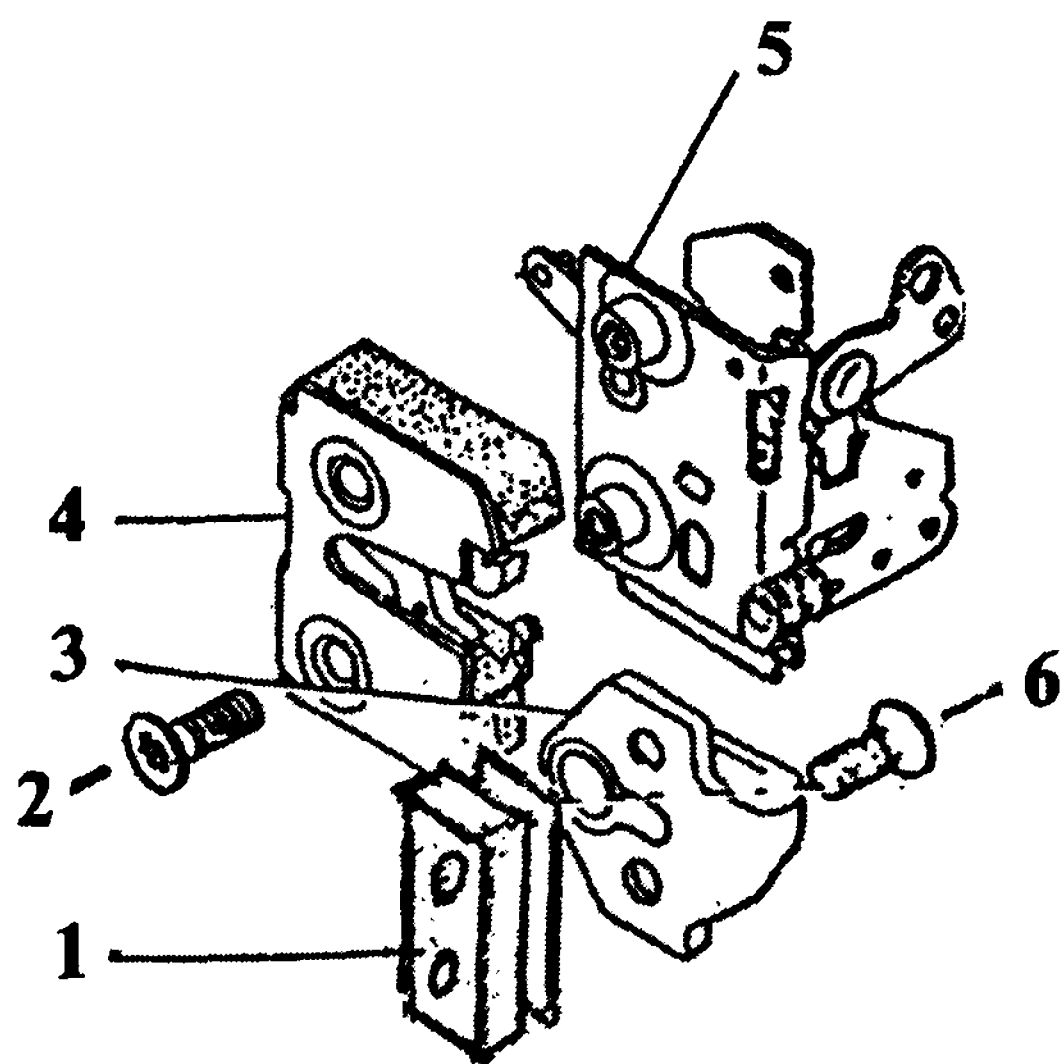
Основные элементы замка: 1 - пластина; 2 - винт крепления запорного механизма; 3 - фиксатор; 4 - запорный механизм; 5 - рычажный механизм; 6 - винт крепления фиксатора; 7 -
